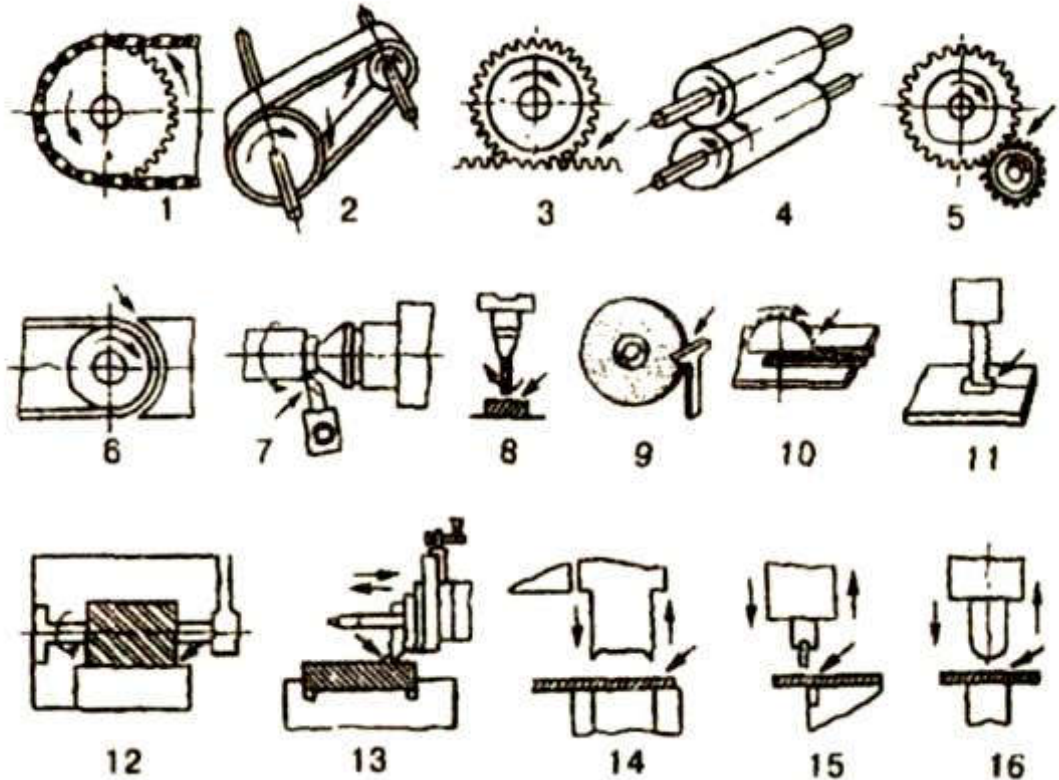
Приклади небезпечних зон механізмів (вказані стрілками): 1 - передаточний ланцюг із зубчаткою; 2 - пасова передача; 3 - зубчаста рейка; 4 - валки; 5 - зубчатки; 6 - кінець конвеєра; 7 - токарний верстат; 8 - свердло; 9 - абразивний круг; 10 - циркулярна пила; 11 - стрічкова пила; 12 - фрезерний верстат; 13 - поперечно-стругальний верстат; 14 - штампівка; 15 - різання; 16 – загинання.
